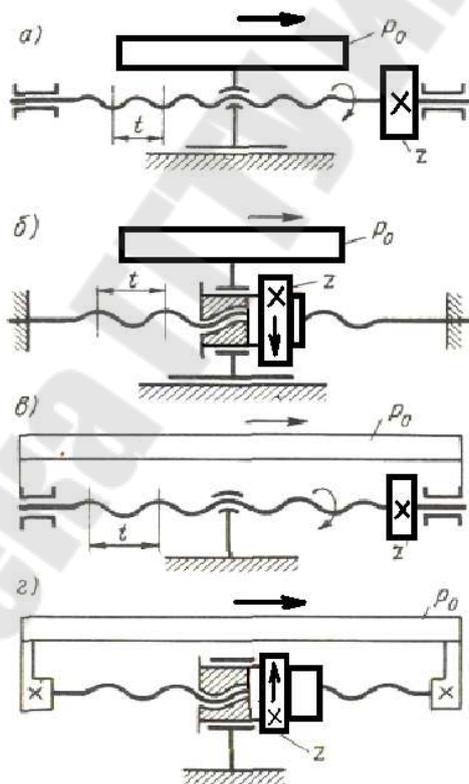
Схема винтовой передачи (передача винт-гайка)
